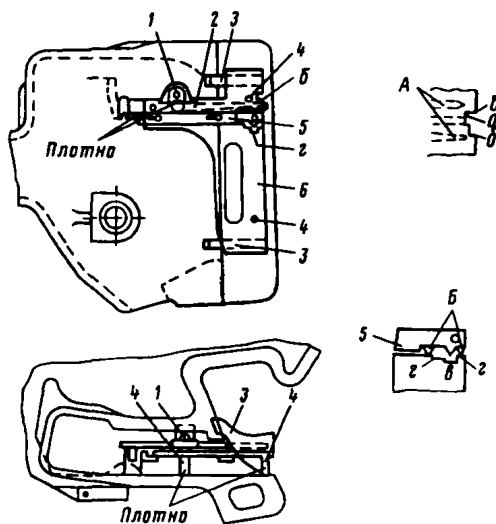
Проверка положения полочки для верхнего плеча предохранителя относительно шипа для замкодержателя и контура зацепления автосцепки шаблоном 834р
